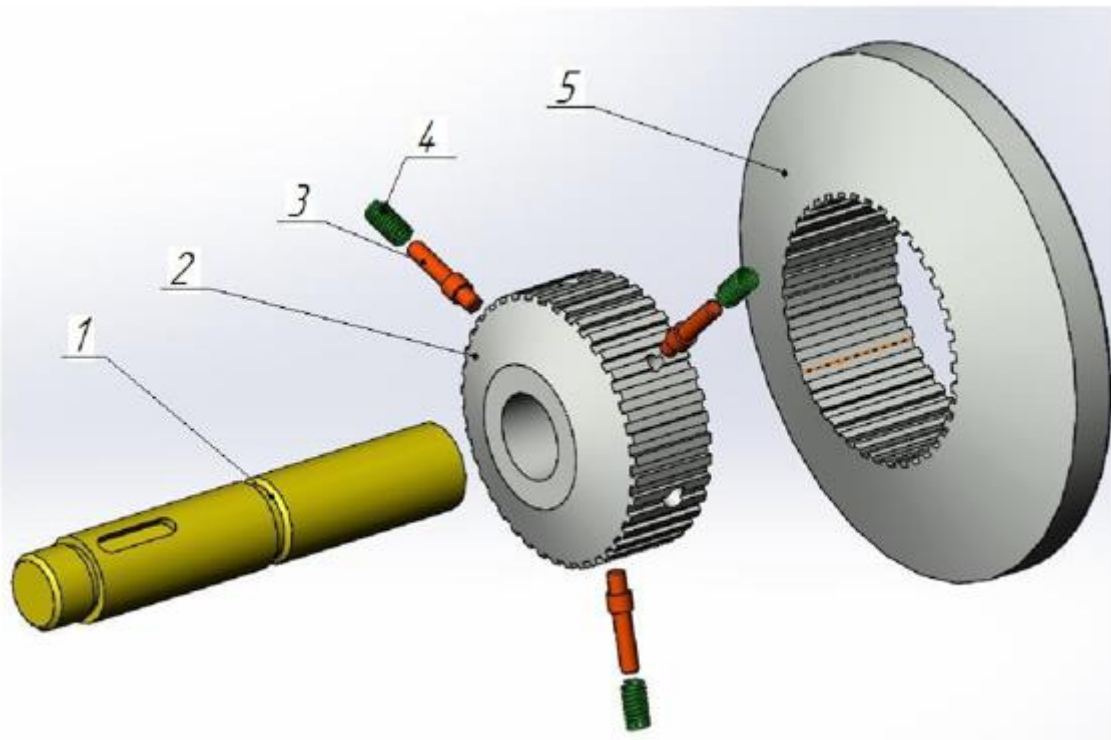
Блокирующее устройство: 1 – проточка на валу; 2 – ступица; 3 – блокирующий штифт; 4 – цилиндрическая пружина; 5 – внешняя секция
